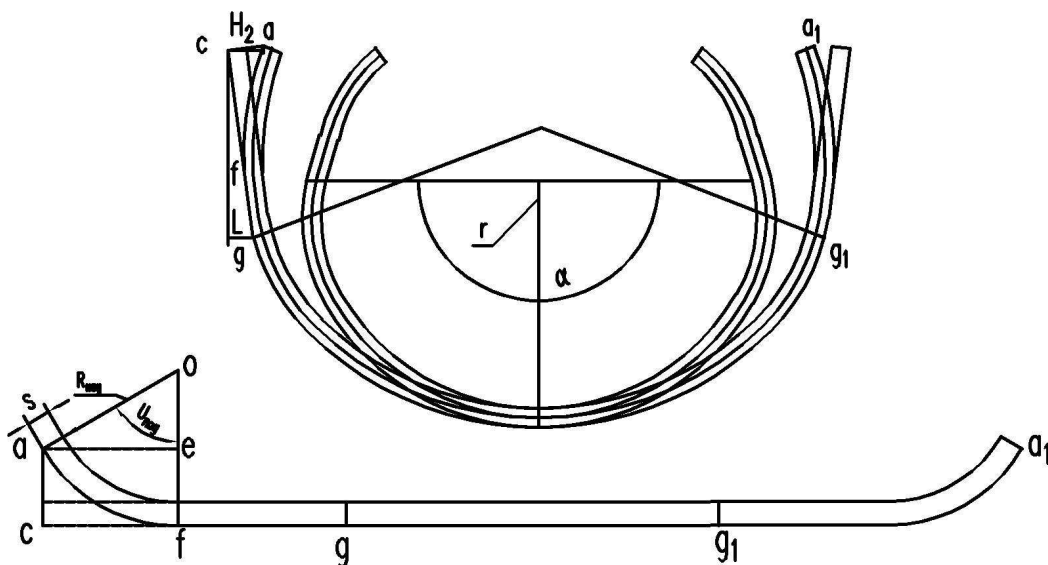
Схема формовки заготовки однорядиусным пуансоном
